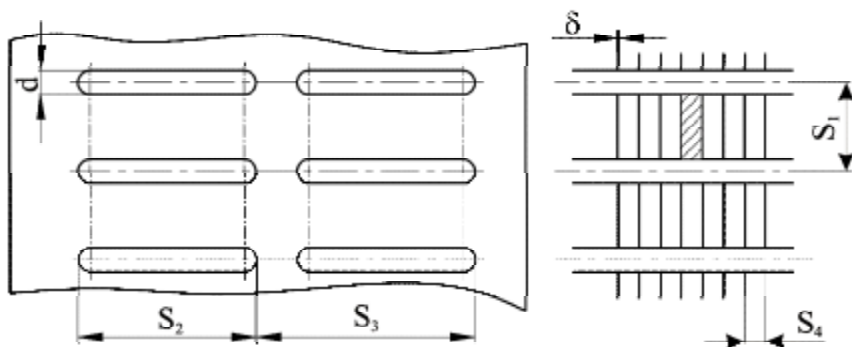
Схема расположения трубок охладителя наддувочного воздуха
